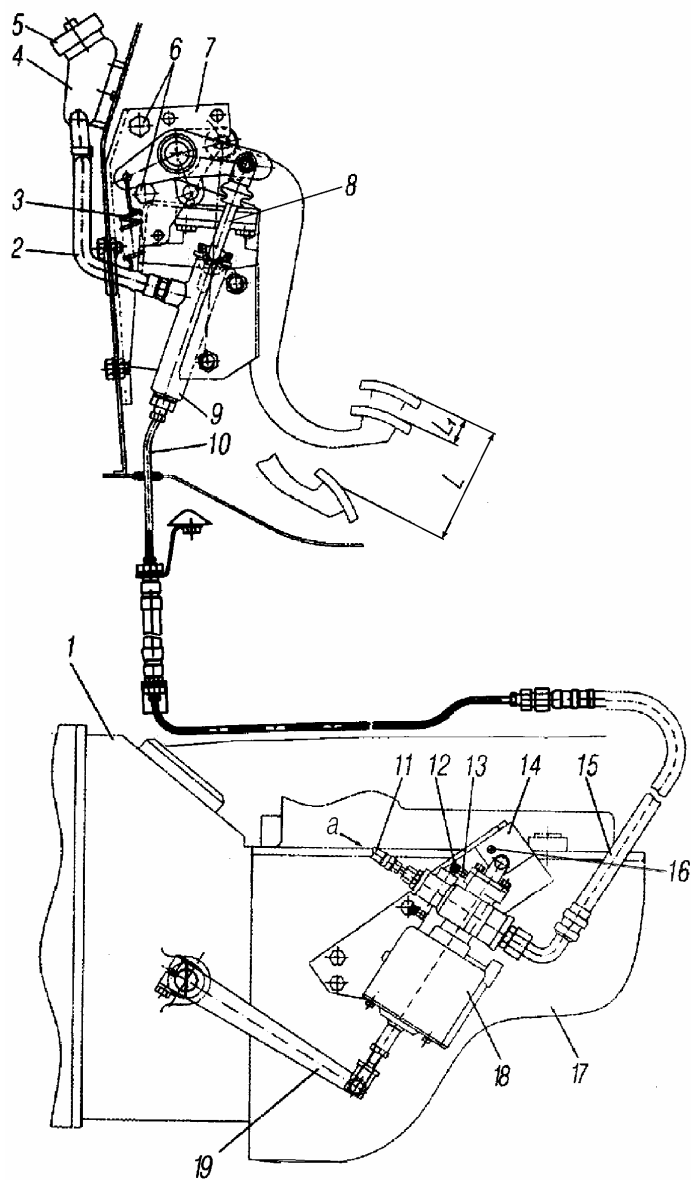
Привод выключения сцепления: 1-картер сцепления; 2-шланг; 3-пружина возвратная; 4-бачок компенсационный; 5-крышка бачка; 6-эксцентрики; 7-кронштейн педального механизма; 8-толкатель; 9-цилиндр главный; 10-трубка; 11-шланг пневматический; 12-колпачок; 13-клапан прокачки; 14-кронштейн ПГУ; 15-шланг гидравлический; 16-болт упорный кронштейна; 17-картер коробки передач; 18-усилитель пневмогидравлический (ПГУ); 19-рычаг вала вилки выключения сцепления; а-от баллона нетормозных потребителей; Л-полный ход педали сцепления и тормоза; Л₁-свободный ход педали сцепления и тормоза
